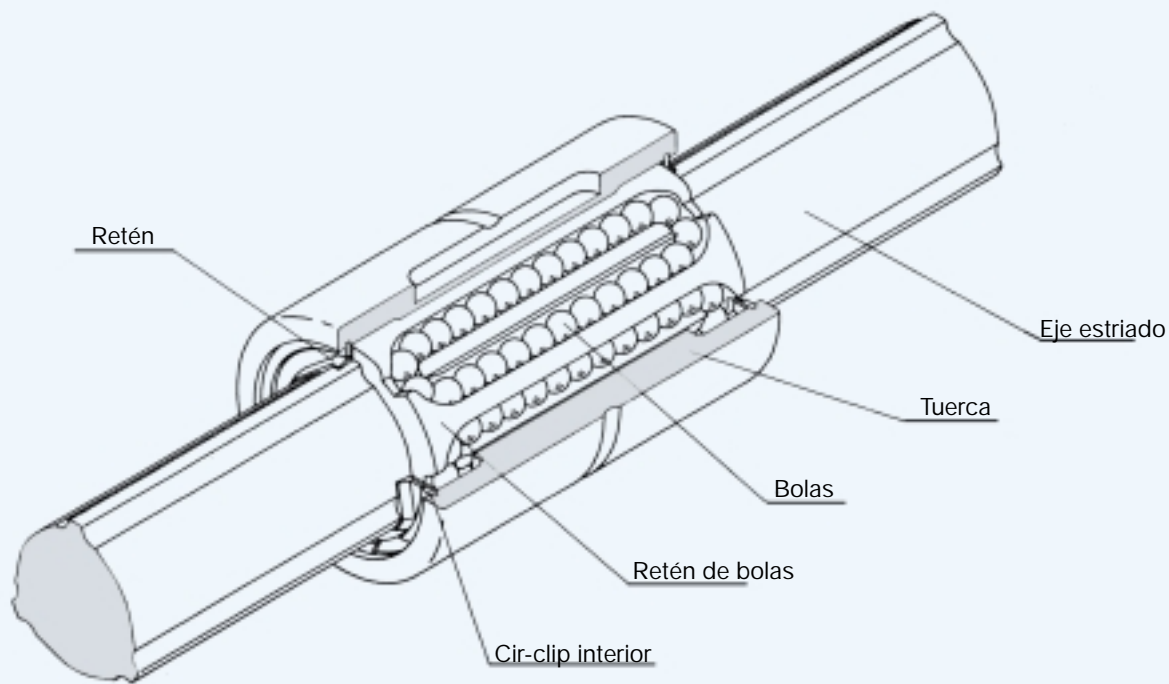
■ Corte transversal del eje estriado de bolas THK tipo LBS.
